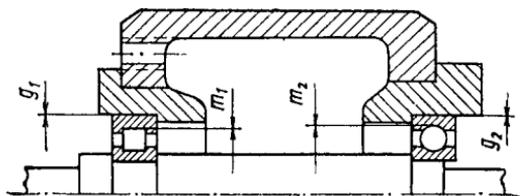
Формуляр контроля подшипников насоса типа X:
